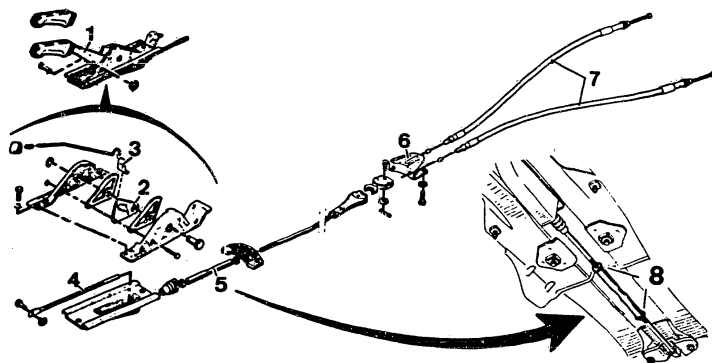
Handbremsmechanismus: 1 Handbremshebel – 2 Hebel – 3 Klinke – 4 Zugstange – 5 Einstellmuffe – 6 Gelenk – 7 Seilzüge – 8 Kontermutter.
